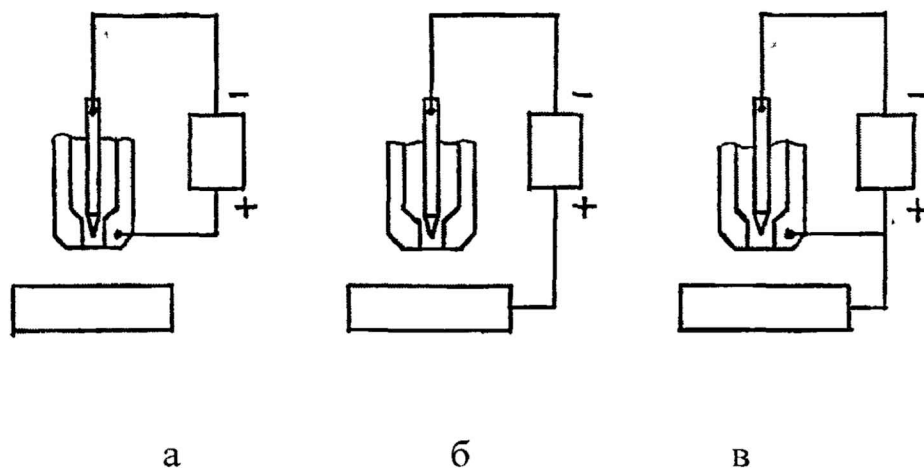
Схеми наплавлення стислою дугою: а - непрямої дії;
